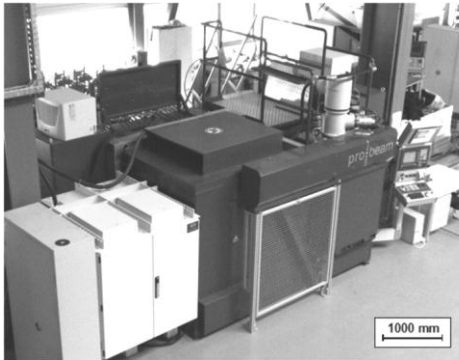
Einkammer-Universalmaschine K7 (links) der pro-beam AG & Co. KGaA sowie deren Prüfkammer (rechts) am Institut für Schweißtechnik und Fügetechnik der RWTH Aachen (ISF Aachen)
